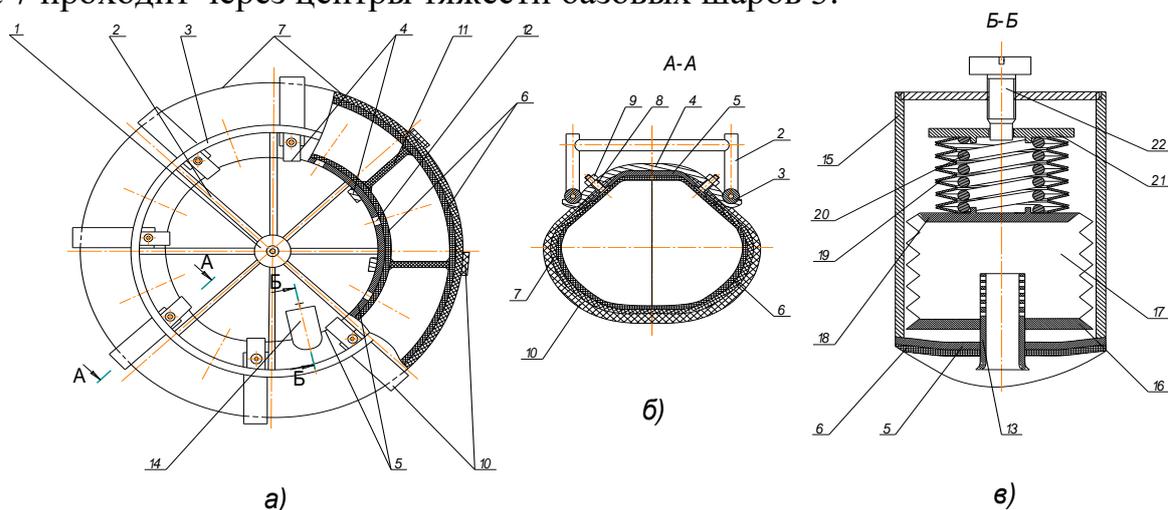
Колесо низкого давления и повышенного демпфирования: а) общий вид колеса сбоку, выполненный с разрезом; б) разрез А-А; в) разрез Б-Б; 1 – ступица; 2 – спицы; 3 – ободья; 4 – ложементы; 5 – диск; 6 – камера; 7 – шина; 8 – болт; 9 – гайка; 10 – грунтозацепы; 11 – перегородка; 12 – радиальное отверстие; 13 – дросселирующая трубка; 14 – пневматический демпфер; 15 – корпус; 16 – неподвижное основание; 17 – камера сильфонная; 18 – подвижное основание; 19 – тарельчатые пружины; 20 – цилиндрическая пружина сжатия; 21 – нажимной диск; 22 – винт
